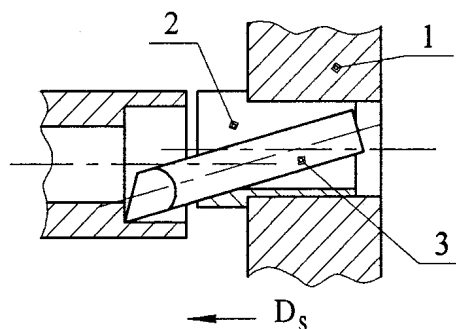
Установка розточувального різця в револьверній голівці:
